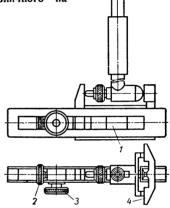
Установка нутромера на заданный размер при помощи плоскопараллельных плиток и приспособления (держателя) для них
